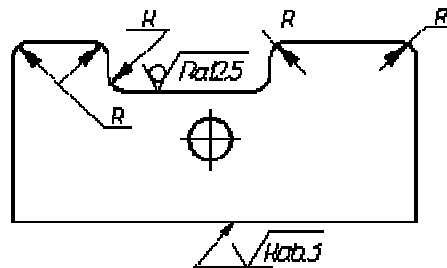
Пример обозначения шероховатости плавно переходящих поверхностей
